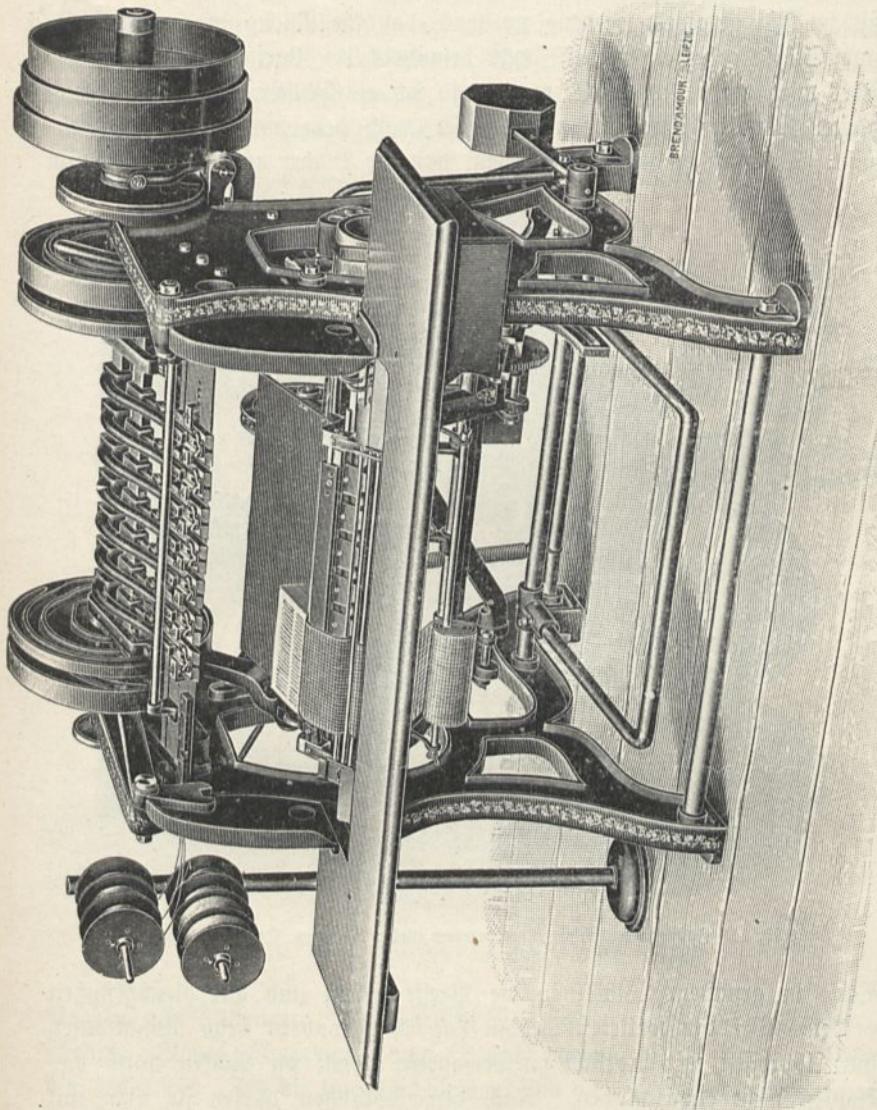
Druckheftmaschine von BRENKE & Co., Leipzig.
